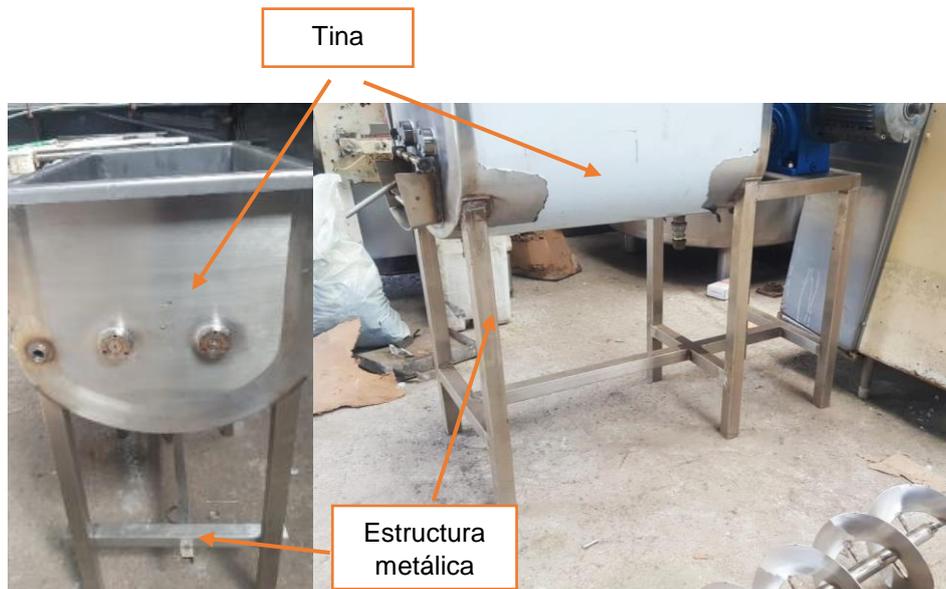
Estructura metálica soldada conjuntamente a la tina.
